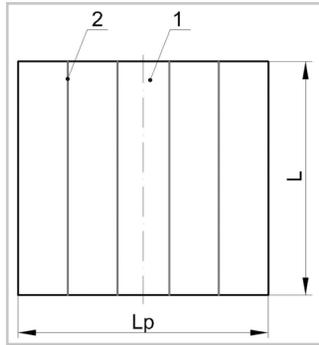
Схема развертки обечайки (листового полотнища): 1 – лист; 2 – сварной шов; L – ширина полотнища (длина обечайки); Lp – длина полотнища (длина развертки обечайки)
